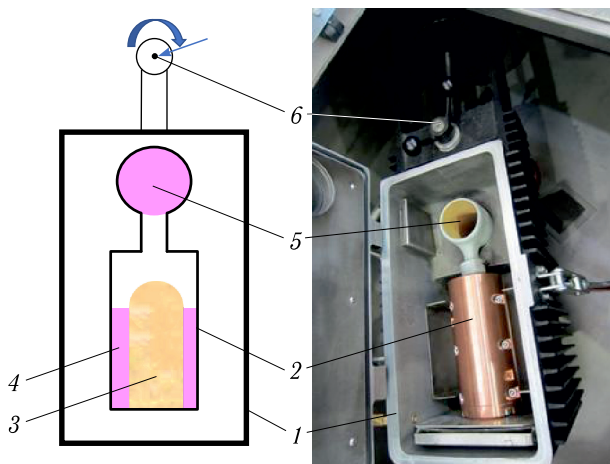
Схема (слева) и внешний вид установки для изготовления Ni-мишени: 1 — вакуумный корпус; 2 — изложница; 3 — керамический стержень; 4 — ^{58}Ni -мишень; 5 — тигель с исходным никелем; 6 — ось вращения
